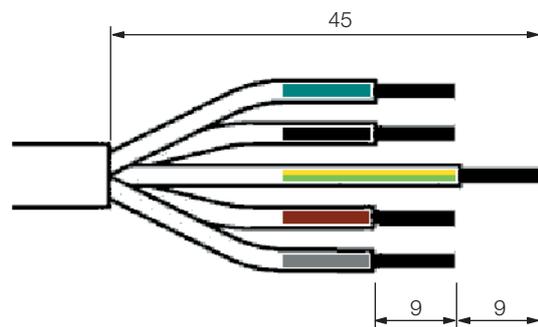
Maße zum Entfernen der Gummiummantelung und der Isolierung
